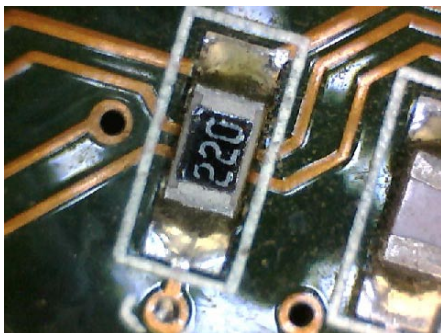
Zobrazení konvexní (vyduté) a konkávní (duté) plochy
